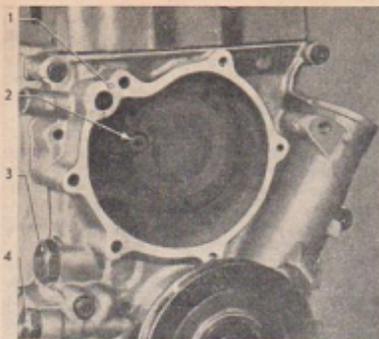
»Versteckte« Steuergeläuseschraube hinter der Wasserpumpe
